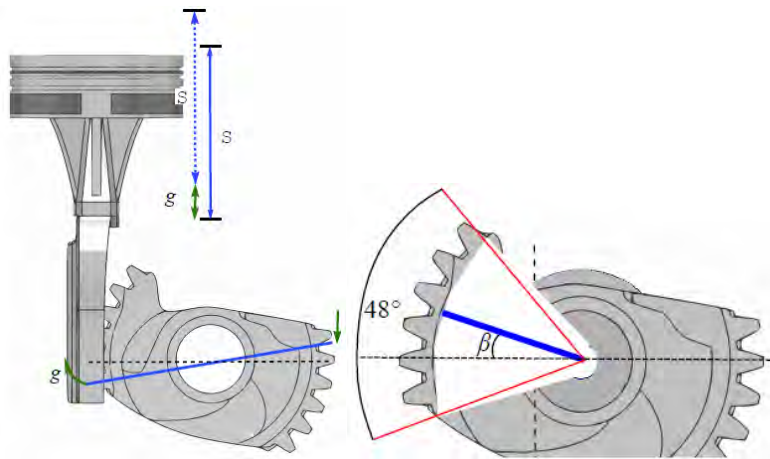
Movimiento engranaje de transmisión - pistón de combustión y Ángulo instantáneo β y apertura máxima del engranaje de transmisión
